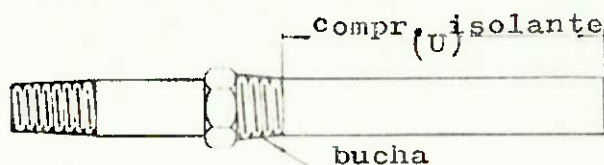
TUBO PROTETOR COM BUCHA DE MONTAGEM
